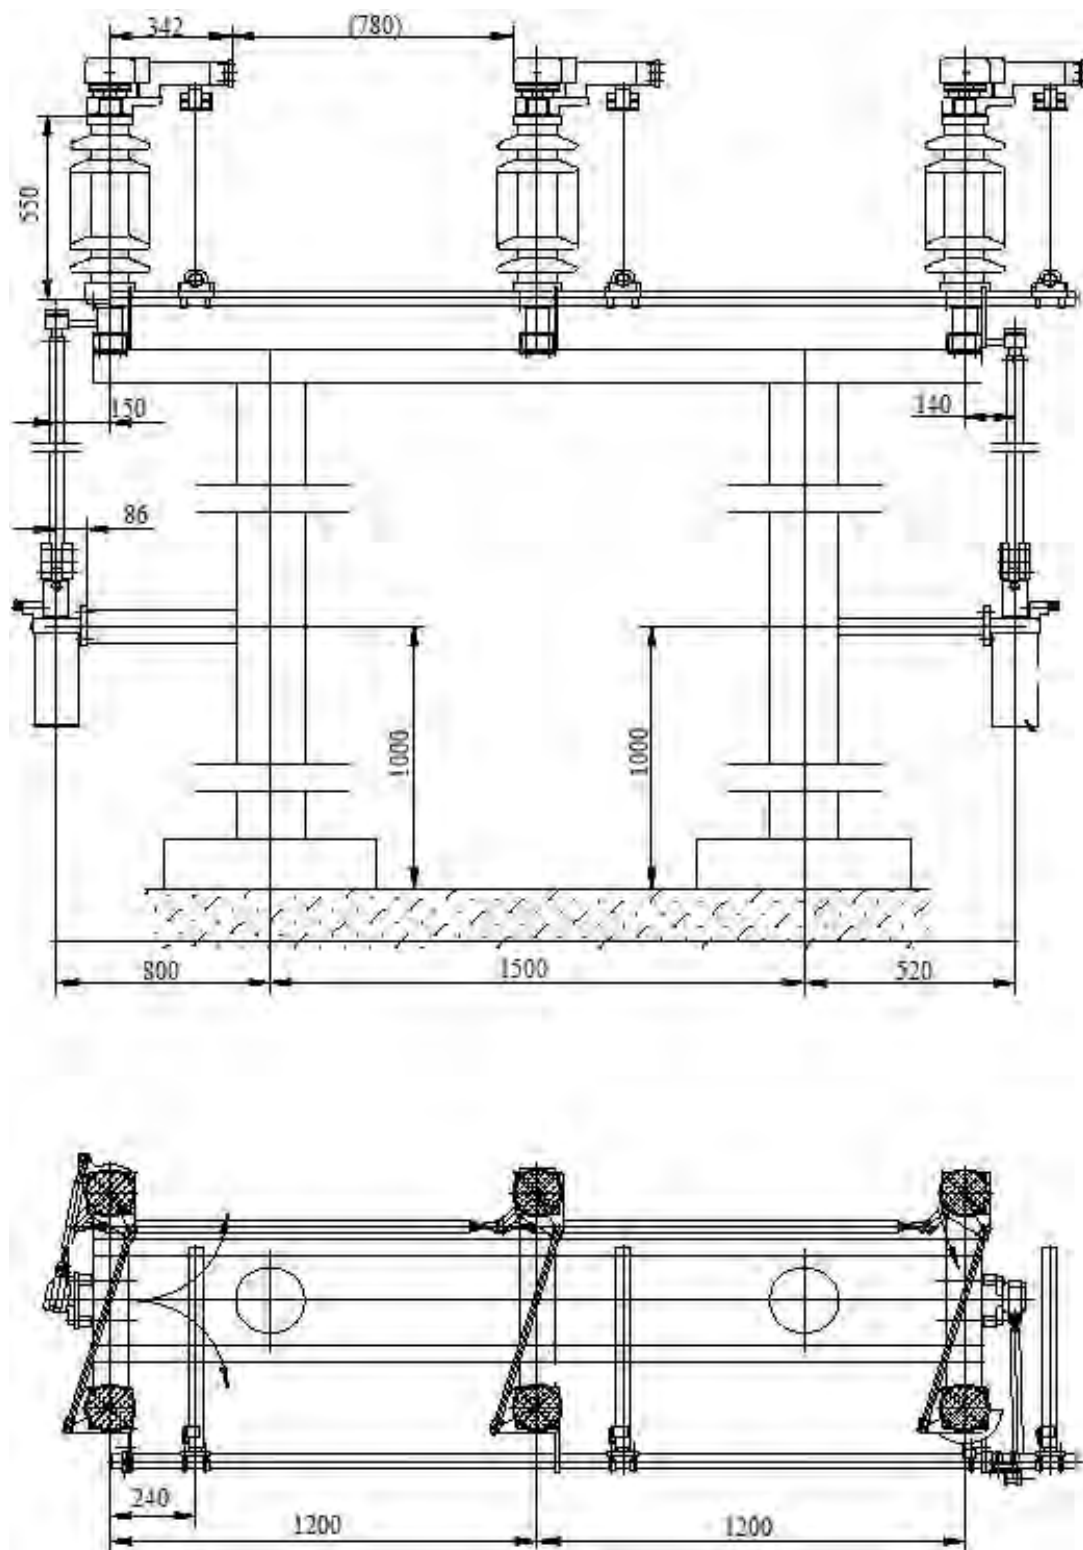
Габаритные размеры и конструктивное исполнение разъединителя РГП на напряжение 35 кВ
